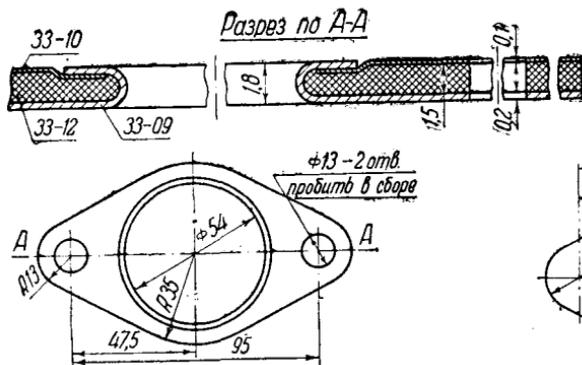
Дет. № 33-К1. Прокладка глушителя
